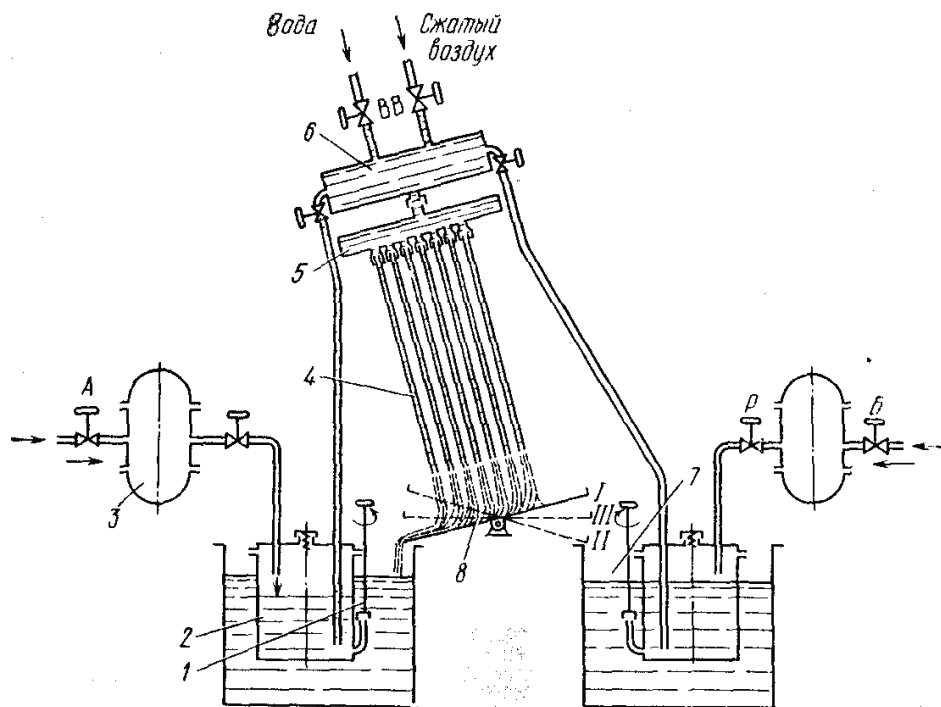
Схема работы установки для комбинированной очистки внутренних поверхностей металлических трубок
